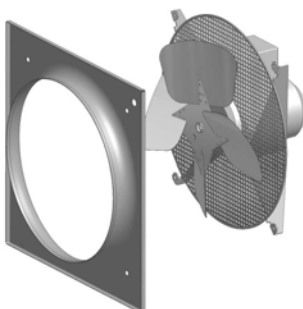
Ventilator in druckgekapselter Ausführung mit kurzer Einströmdüse
